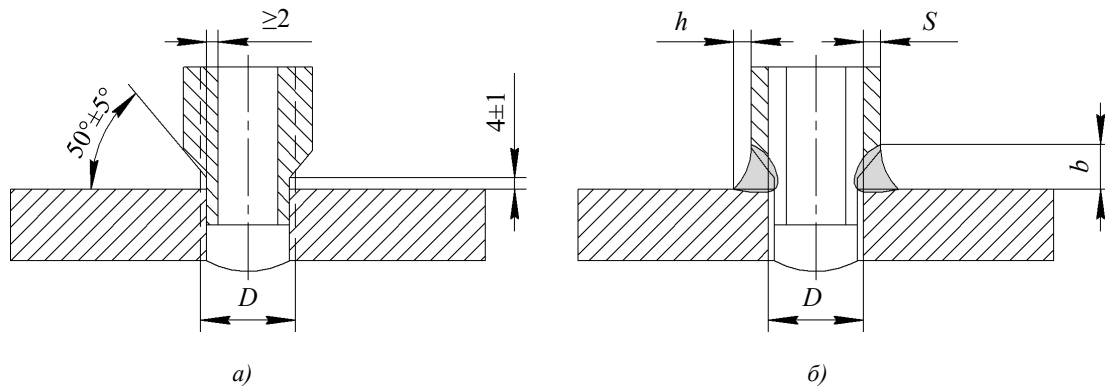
Штуцерный узел: а — до сварки; б — после сварки и удаления корня шва
